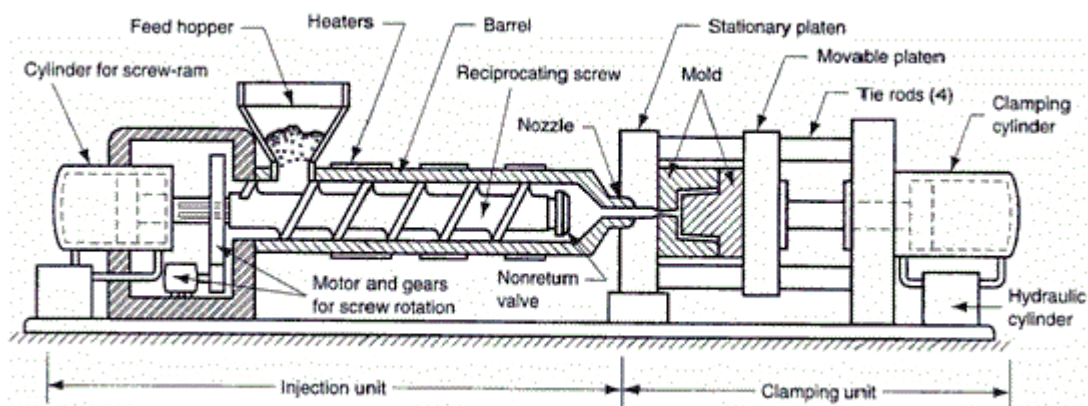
Constituintes de uma máquina de injeção (adaptado de https://www.alibaba.com/product-detail/plastic-injection-moulding-machine-with-price_60061594617.html n.d.)
